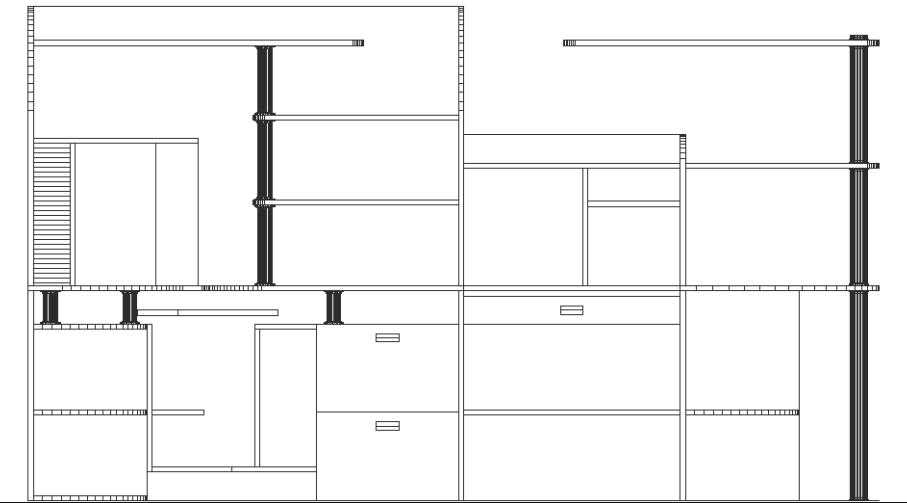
▼ Главный вид с обозначенными криволинейными поверхностями
